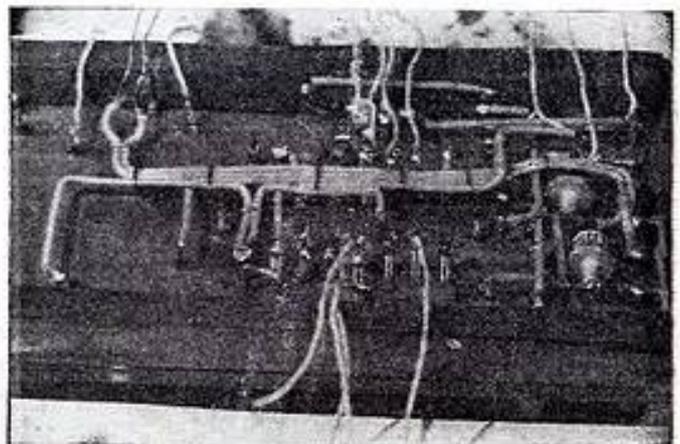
Vue générale du dessous. On remarque les « sorties » en fils souples.
